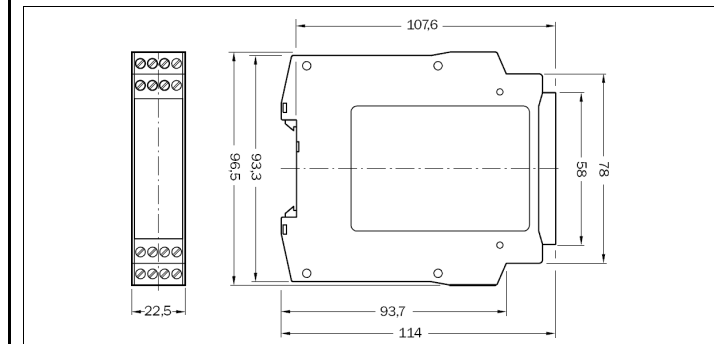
Croquis de dimensiones UE42-2HD con terminales extraíbles (mm)
